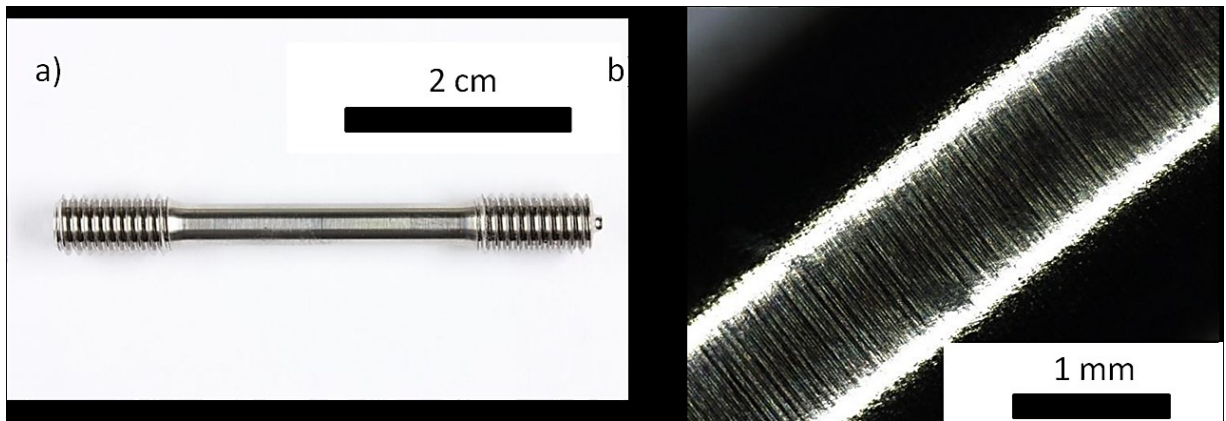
a) Zugprobe B40x20 nach DIN 50125; b) Detailaufnahme der Oberfläche der Zugproben.
